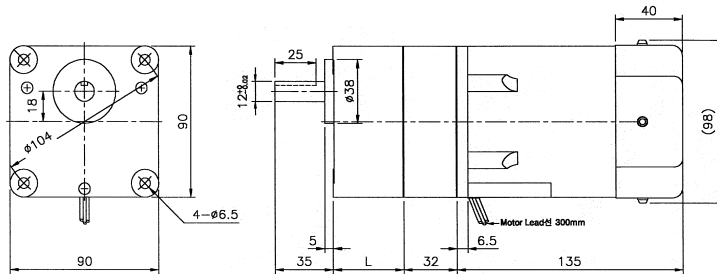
GEARED MOTOR WITH DECIMAL GEAR(中間 GEAR 使用時)
